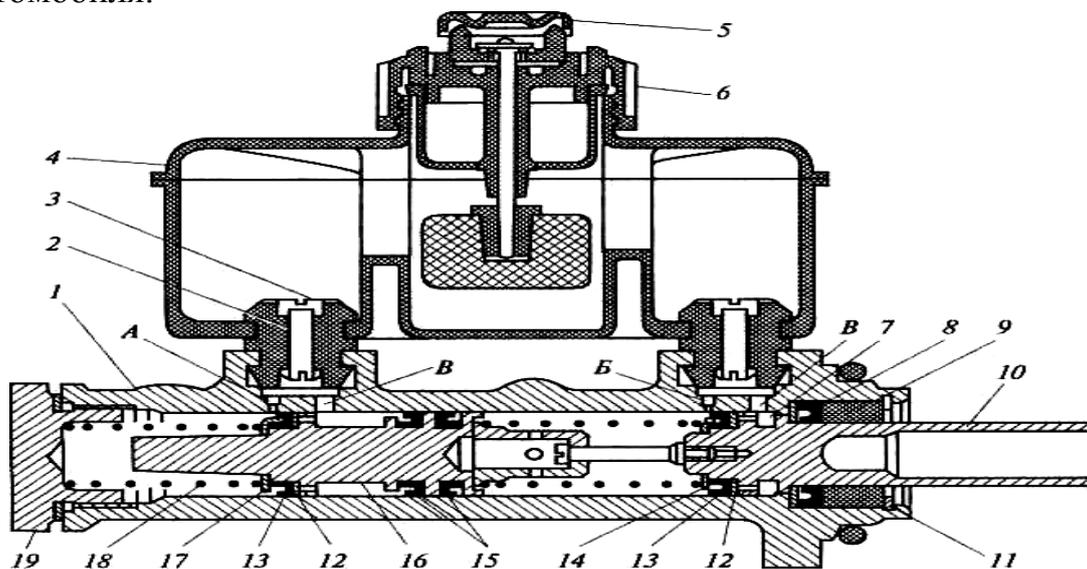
Главный тормозной цилиндр: 1 — корпус; 2 — трубка; 3 — соединительная втулка; 4 — бачок; 5 — защитный колпачок; 6 — ; 7 — упорное кольцо; 8, 14, 17 — упорные шайбы; 9 — направляющая втулка; 10, 16 — поршни; 11 — стопорное кольцо; 12 — шайба поршня; 13, 15 — манжеты; 18 — пружина; 19 — пробка; А, Б — компенсационные отверстия; В — перепускные отверстия
